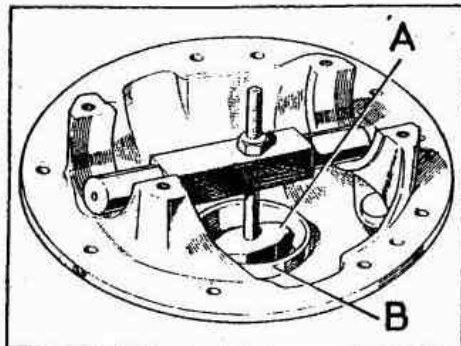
Desmontaje a presión de la pista exterior de rodamiento
